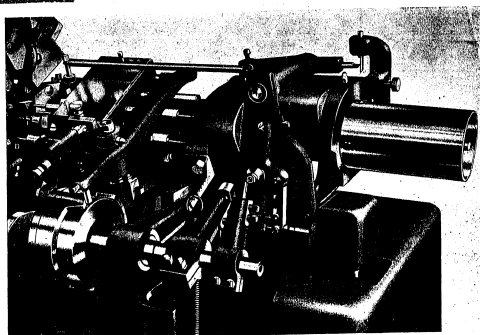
SCHWENKBARER WERKZEUGKOPF HW-17
